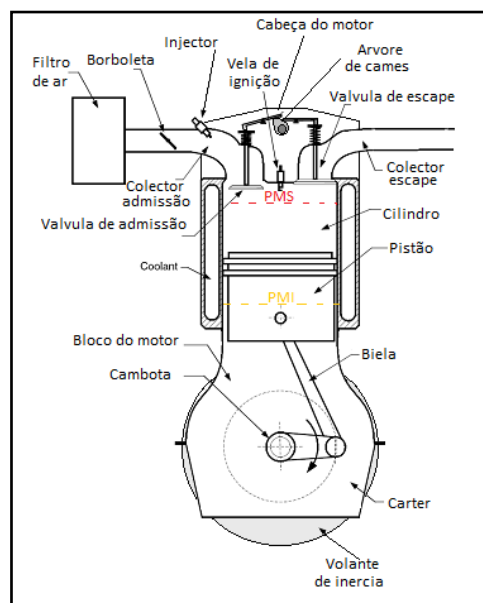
Esquema de um motor de combustão interna monocilíndrico.
